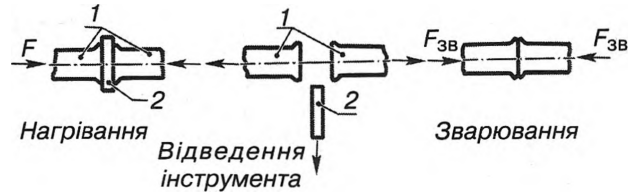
Схема контактної теплової зварювання нагрітим інструментом:
